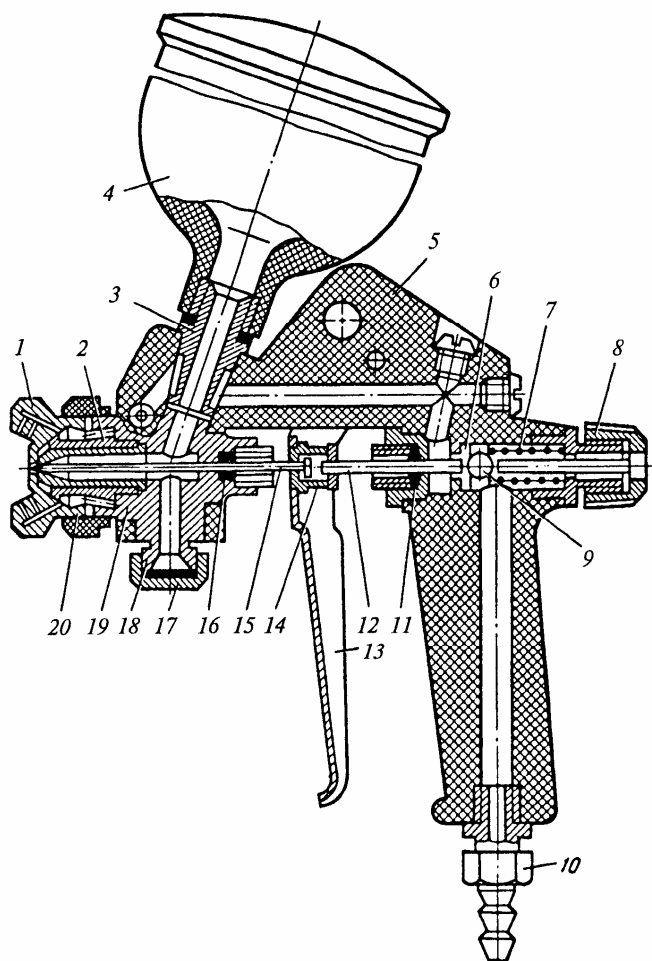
Краскораспылитель с верхним бачком: 1 – воздушная головка; 2 – распределитель воздуха; 3, 18 – штуцера; 4 – бачок для краски; 5 – корпус; 6 – седло клапана; 7 – пружина; 8 – винт для регулирования расхода лакокрасочного материала; 9 – шарик; 10 – штуцер для подачи воздуха; 11, 16 – уплотнения; 12 – шток; 13 – пусковой курок; 14 – муфта; 15 – запорная игла; 17 – заглушка; 19 – краскопровод; 20 – накидная гайка
